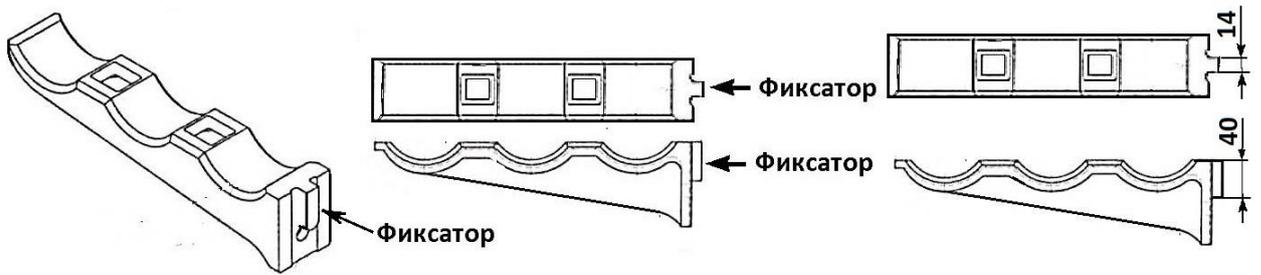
Размеры фиксаторов консолей ККЧ.
